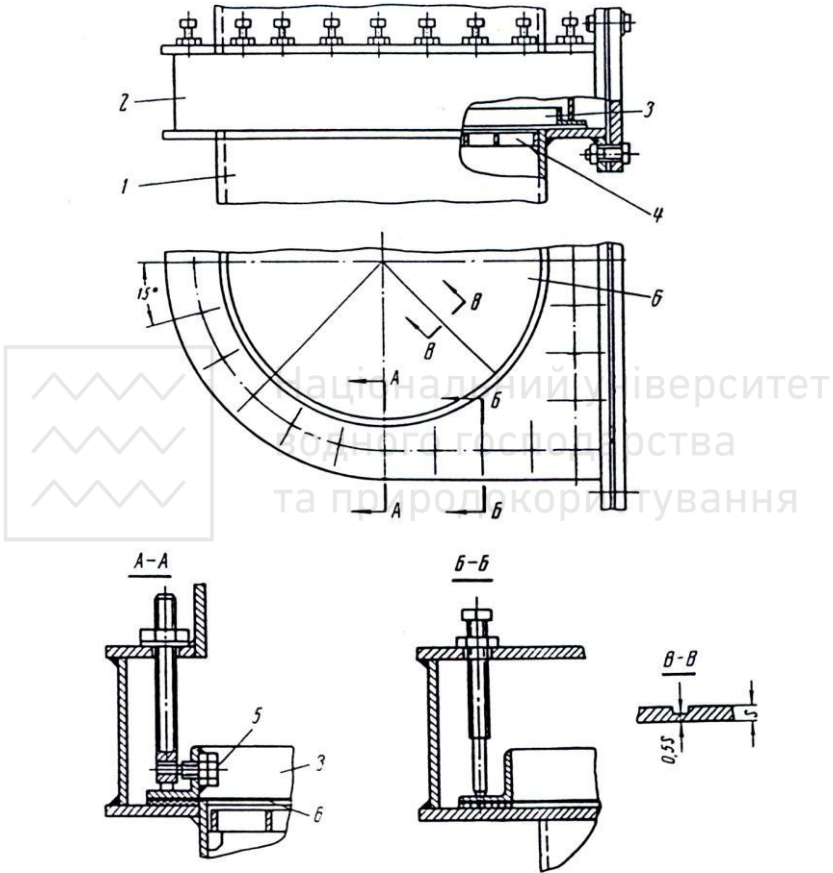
Горизонтальний вибуховий клапан: 1-труба сушарки; 2-корпус вибухового клапана; 3-рамка кріплення діафрагми; 4-решітка; 5-фіксатор; б-діафрагма
